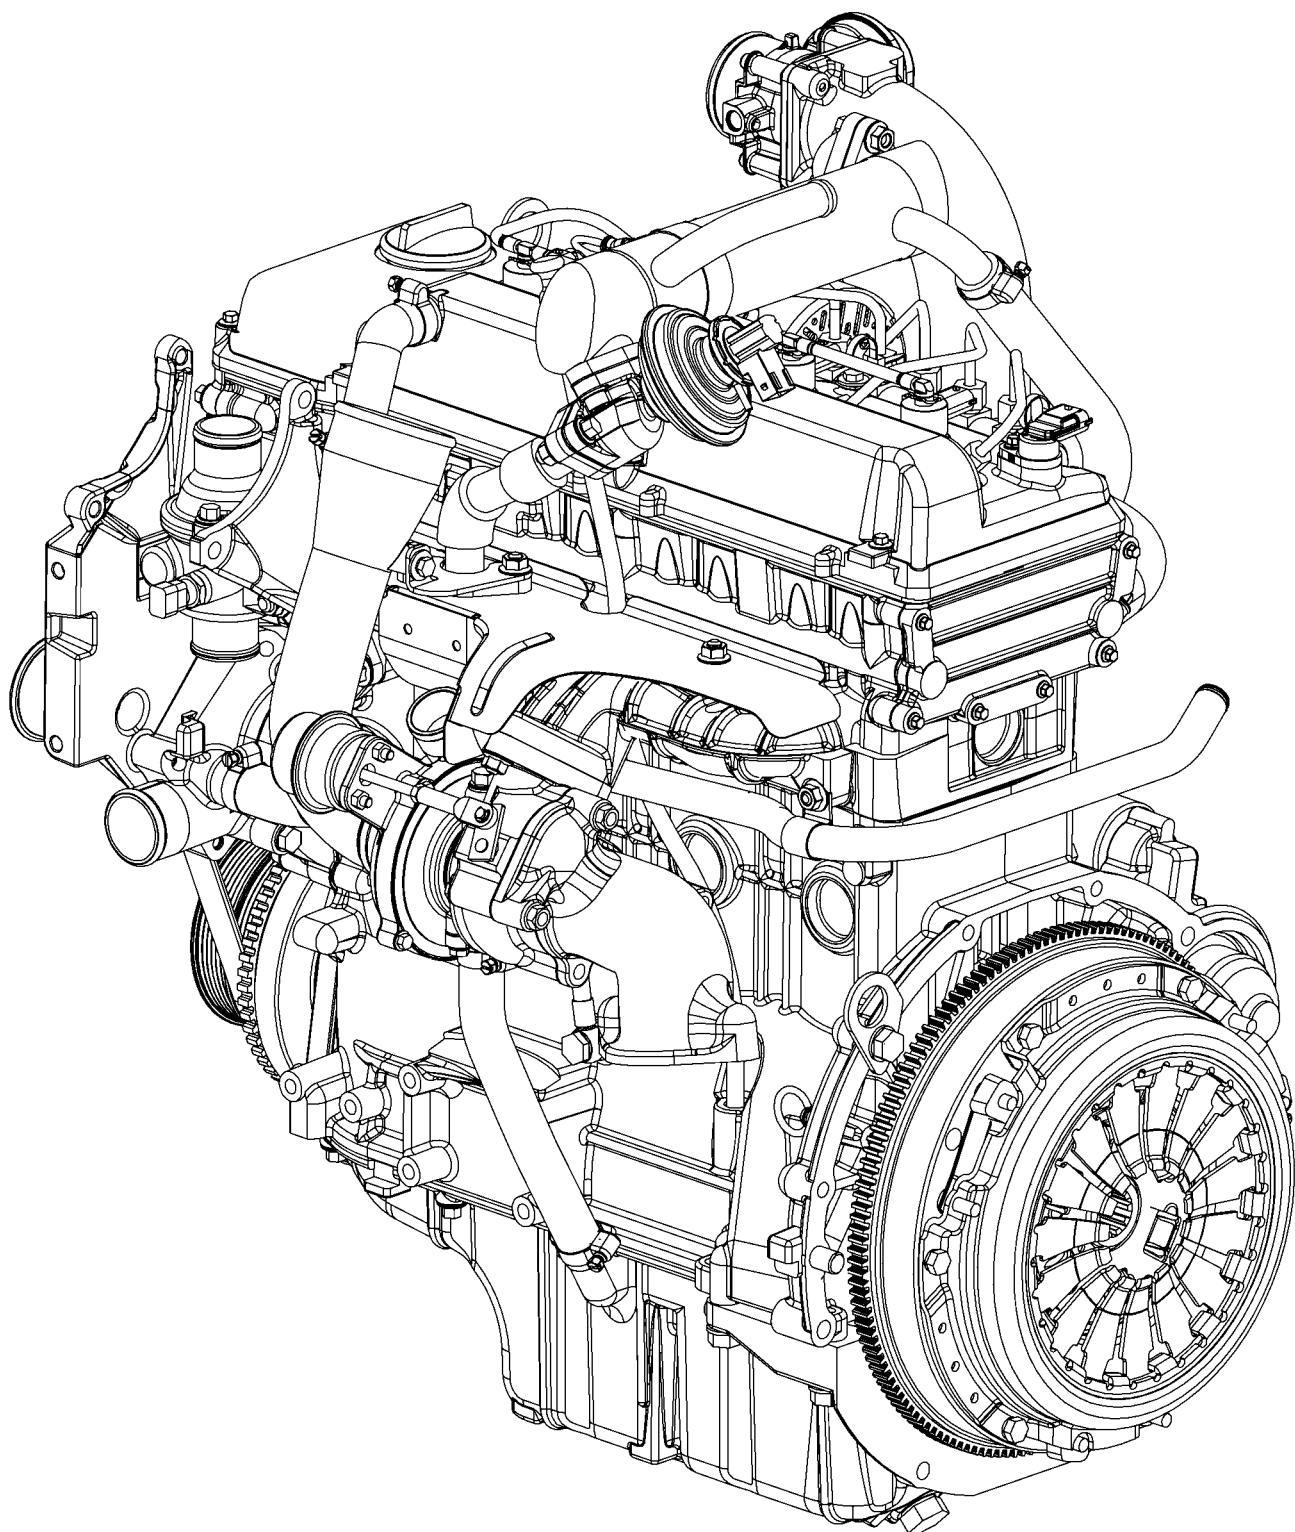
Внешний вид двигателя без компрессора кондиционера, насоса ГУР и деталей привода вентилятора
